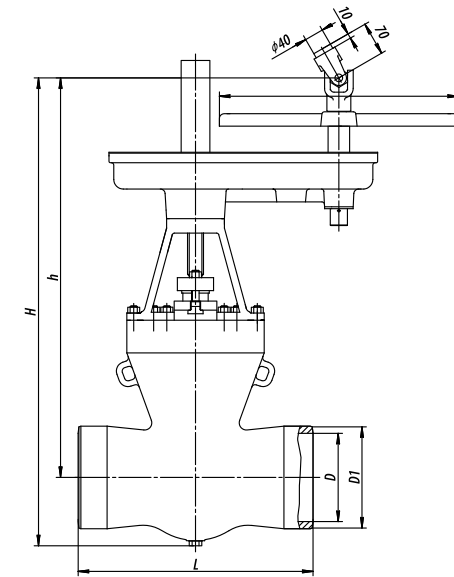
Задвижка DN150...400 с цилиндрическим редуктором
